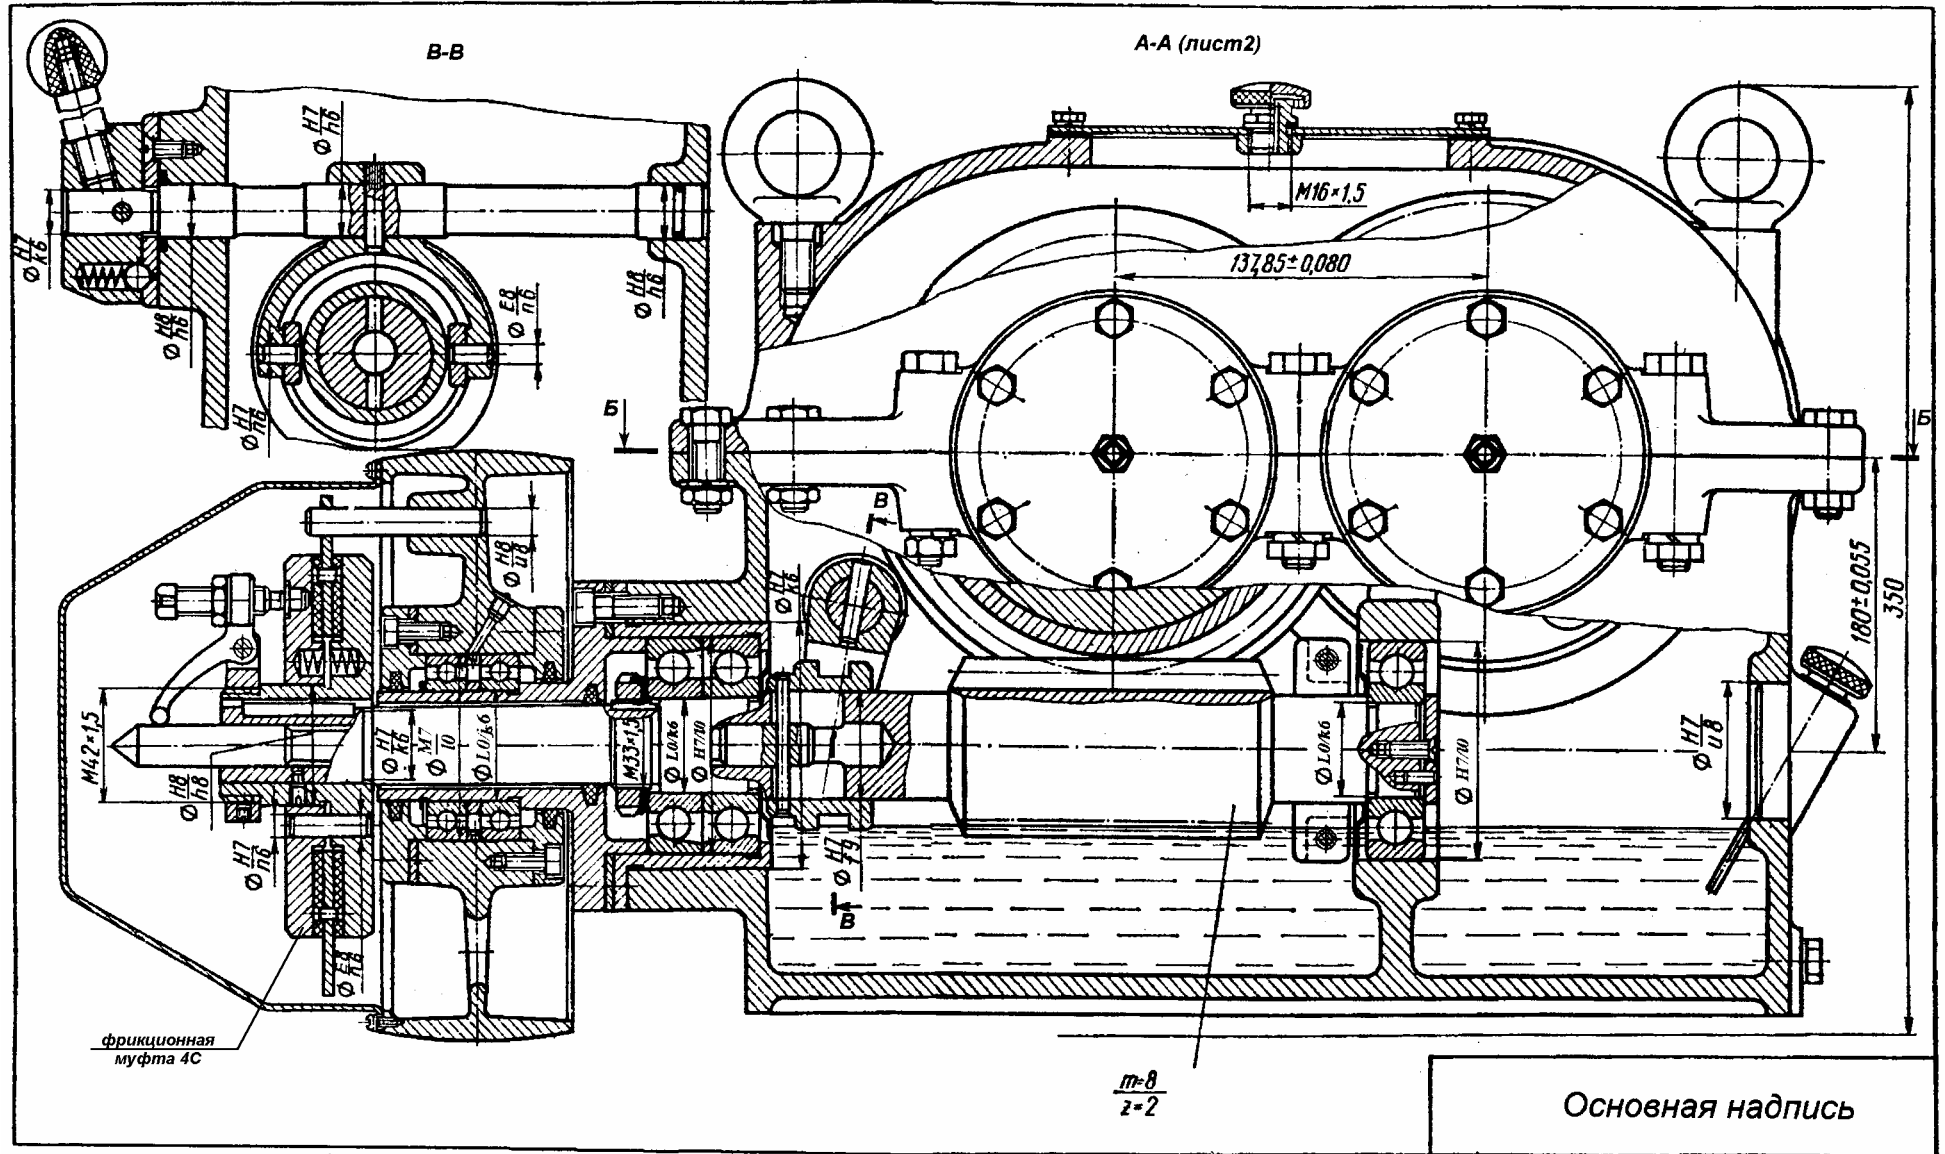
Редуктор червячно-цилиндрический (лист 1)
